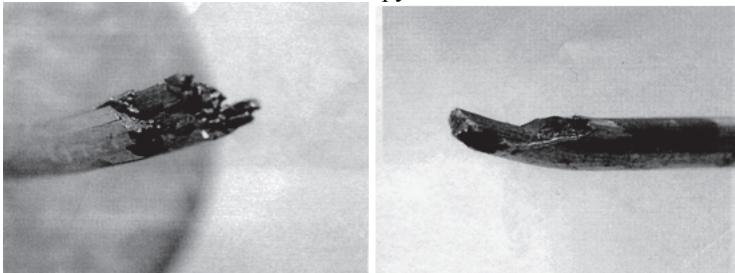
Внешний вид хрупкого разрушения пружин из проволоки диаметром 2,20 мм.
